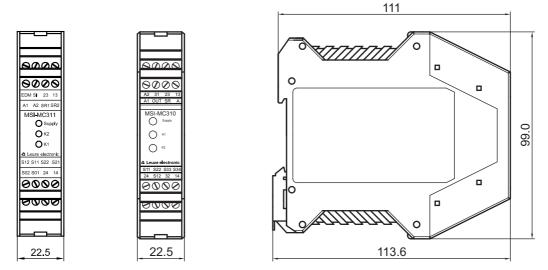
Dimensioni modulo di sicurezza MSI-MC310/MSI-MC311
